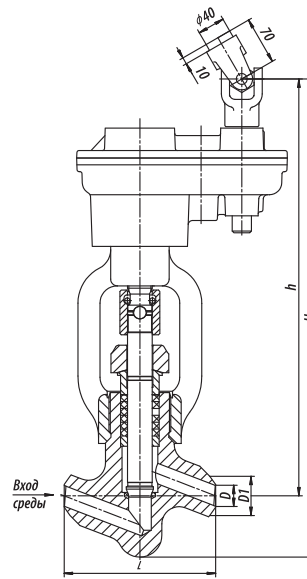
а. Клапан запорный DN32-65 с цилиндрическим редуктором
